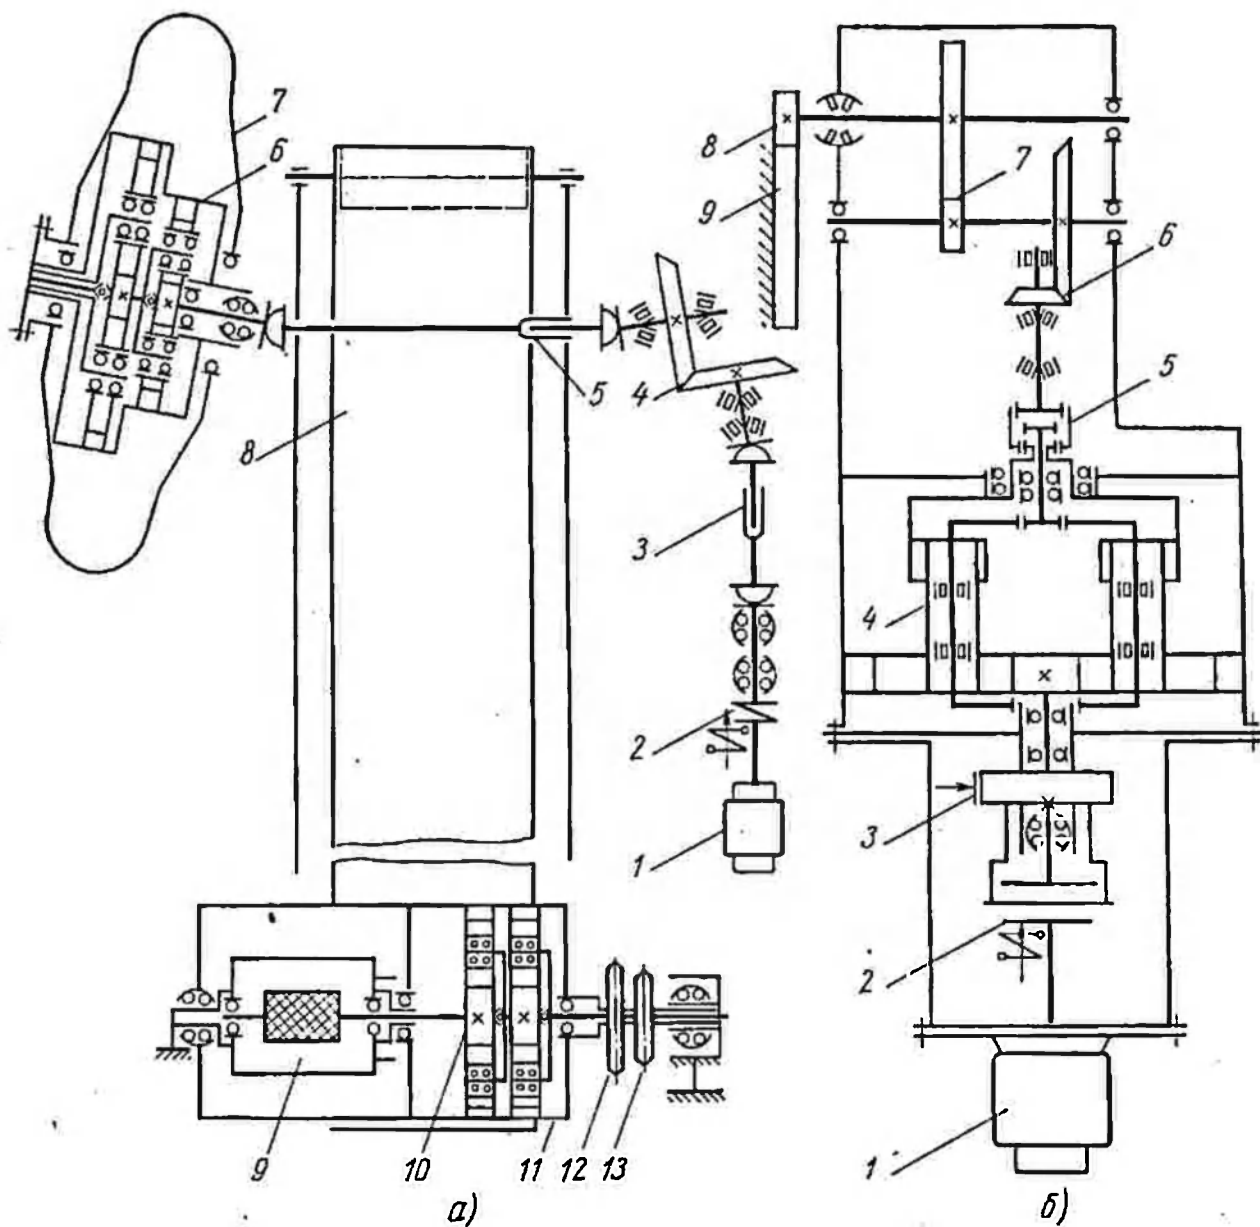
Кинематические схемы механизмов привода роторного экскаватора
